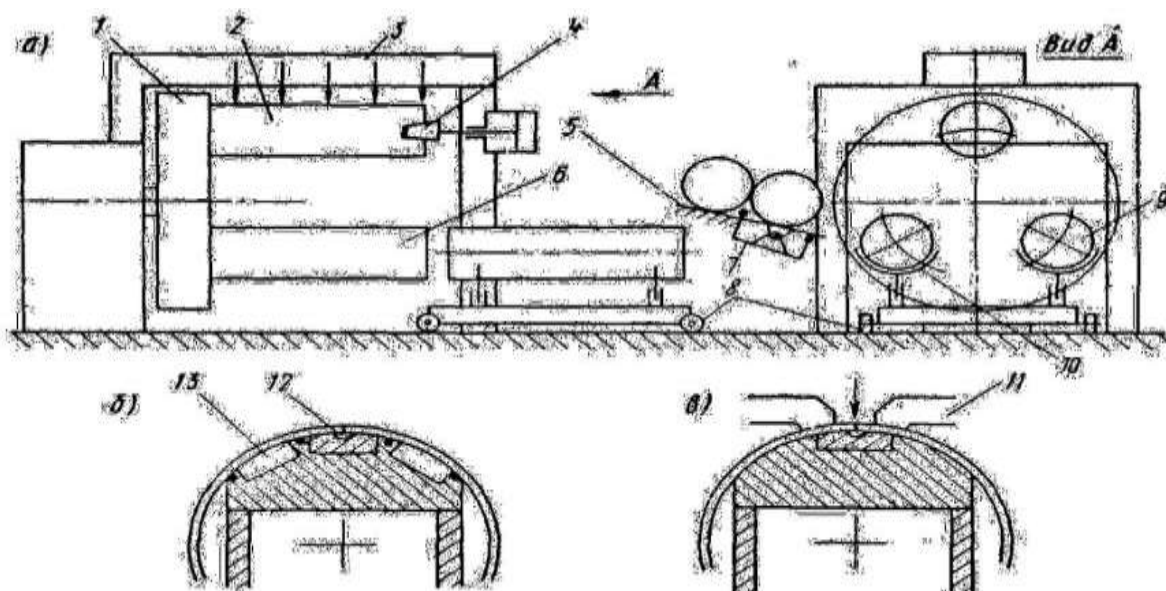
Полуавтоматическая установка для сборки и сварки продольного стыка обечайки
